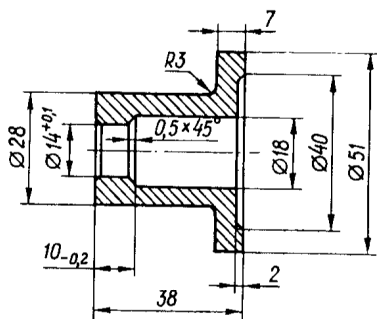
Оправка для выпрессовки и запрессовки наружного подшипника ведущего вала колесного редуктора
